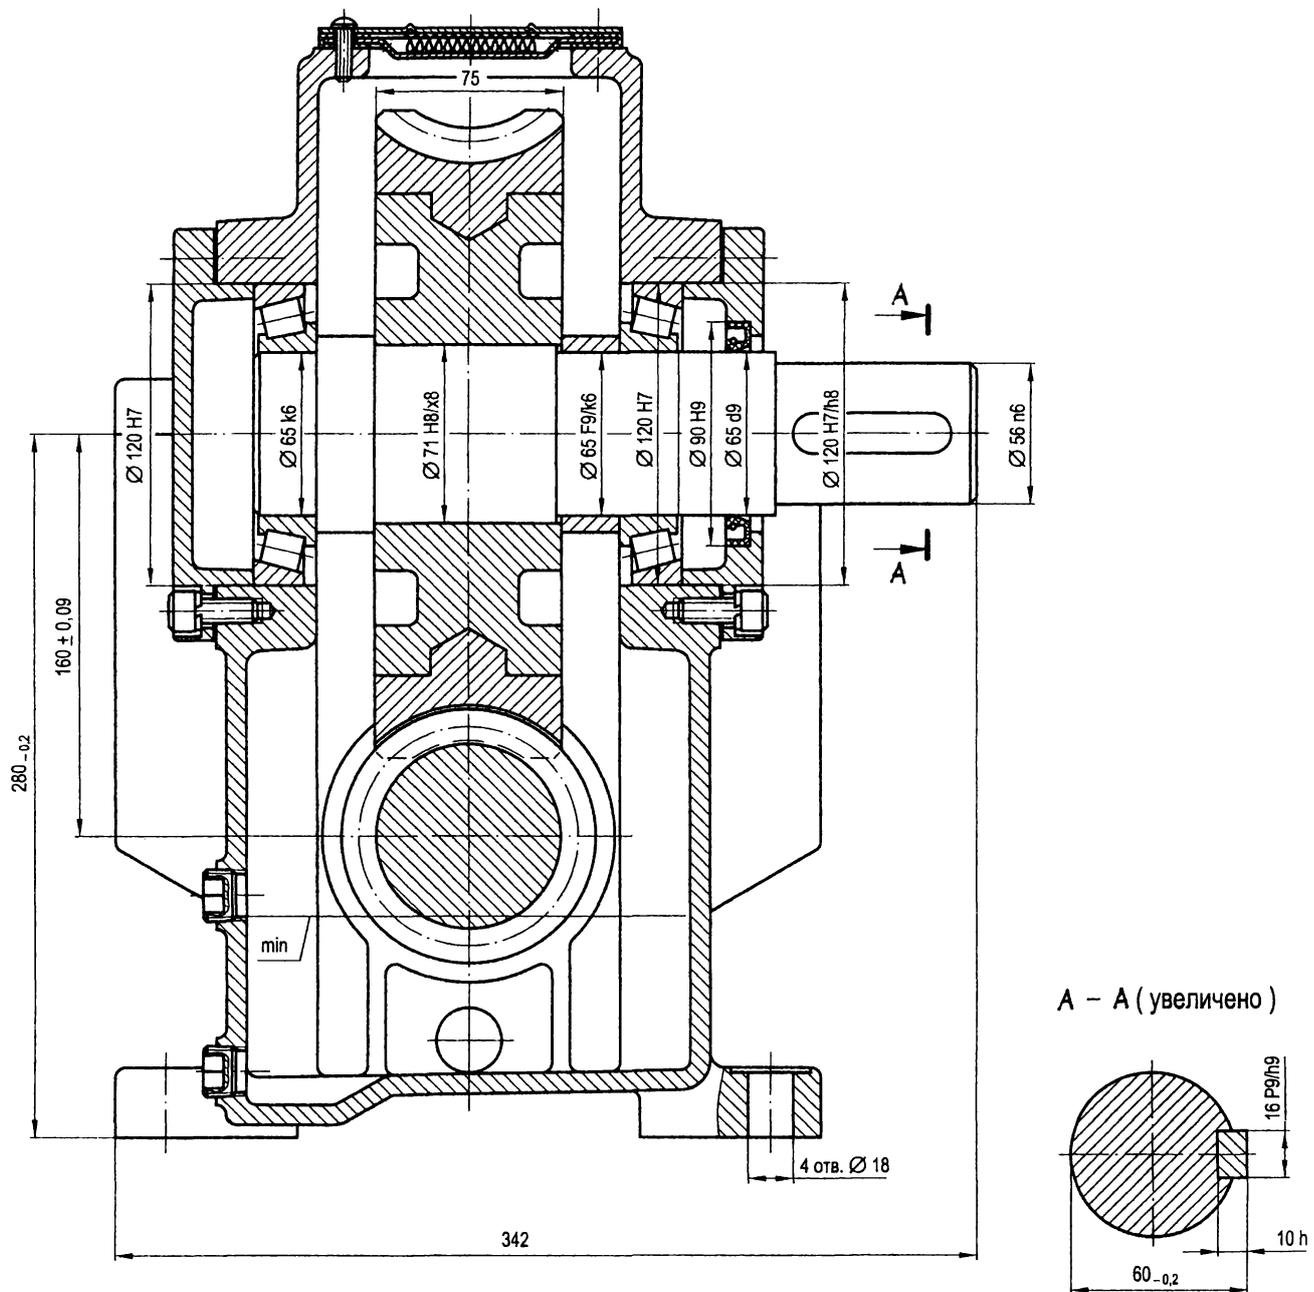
Тихоходный (выходной) вал редуктора с червячной передачей
